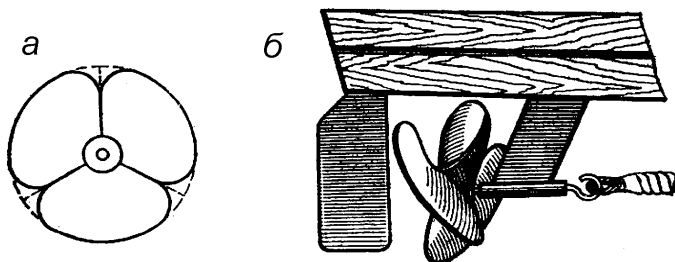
Схема, що показує виготовлення гребних гвинтів для гумових двигунів: а – розкрій гвинта з листа; б – характерна геометрія гвинта і його закріплення в підшипнику
